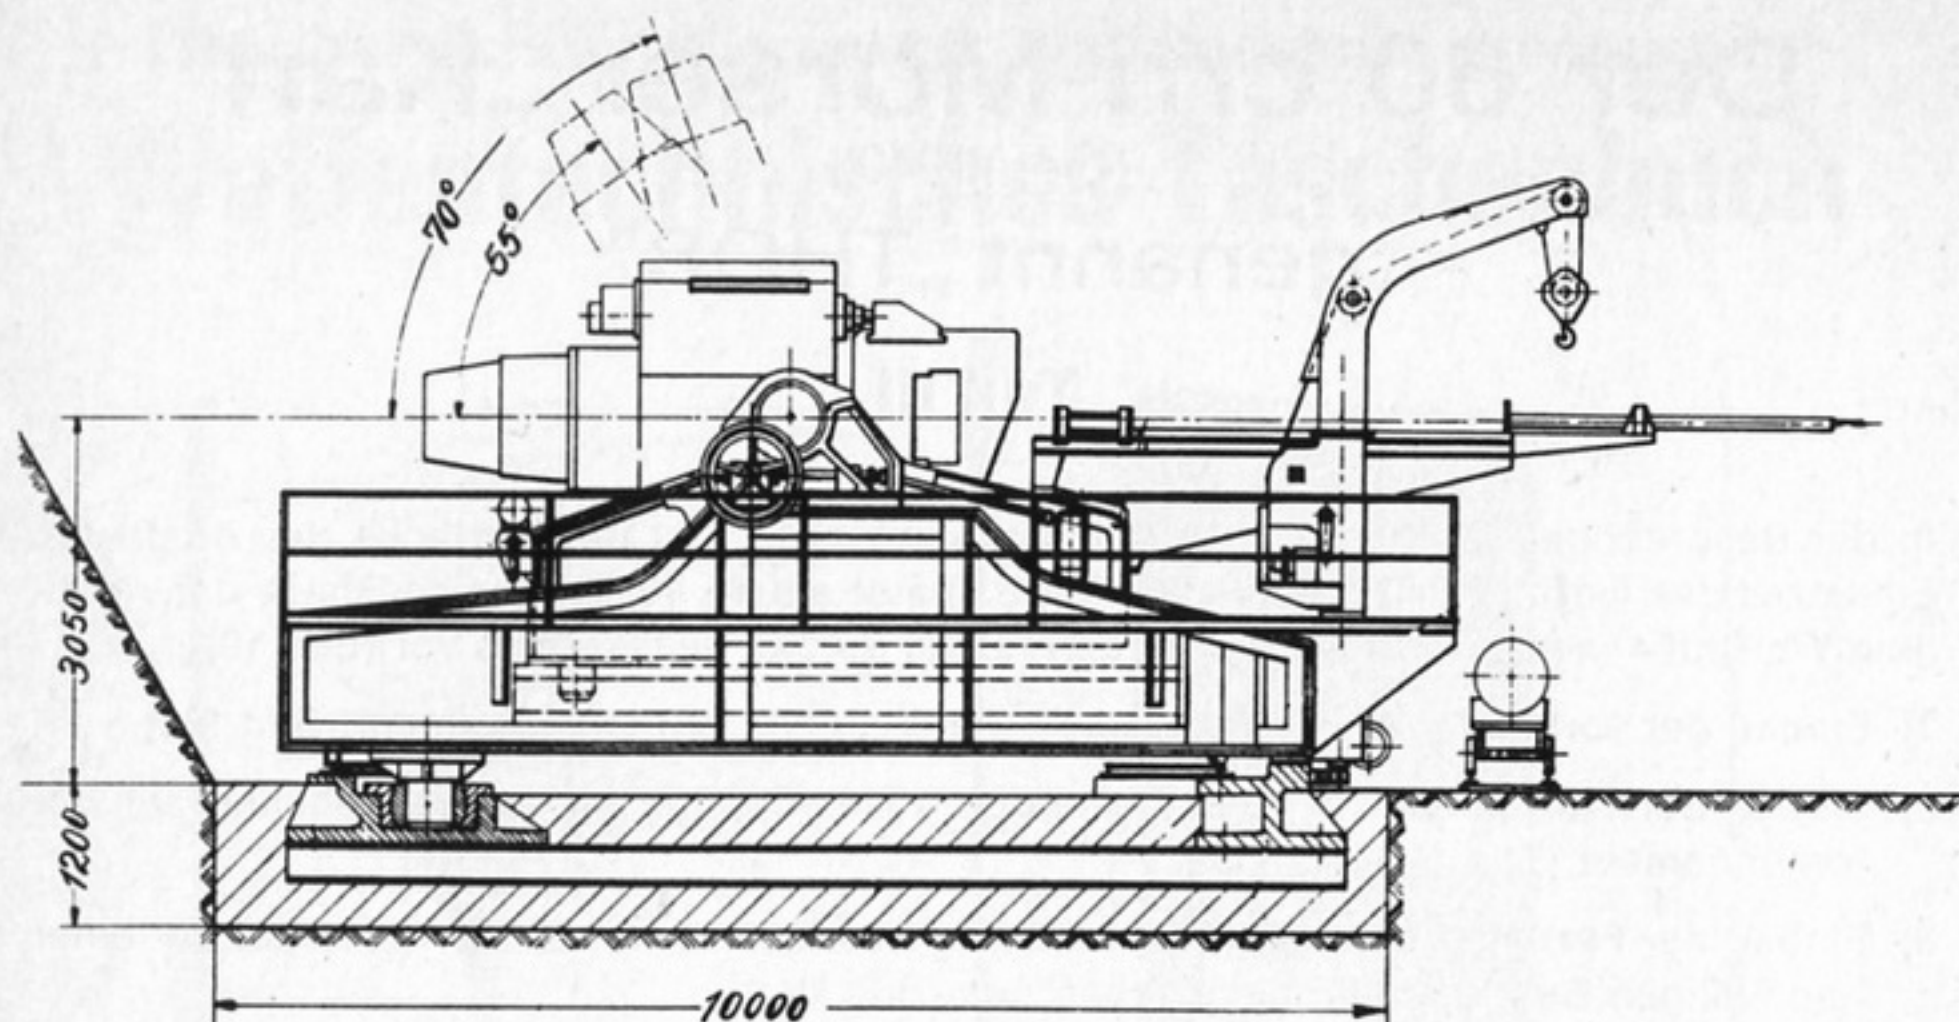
Einbau auf Unterlafette mit Rücklauf auf Betonfundament
